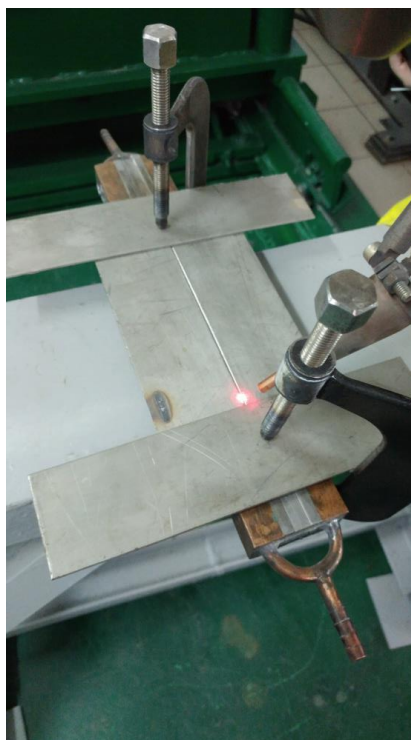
Образец, закреплён на шине и подготовлен под сварку
